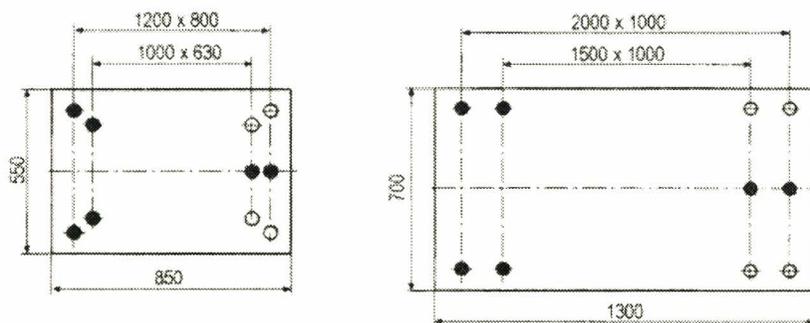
Tipos de apoyos isostáticos para mesas de planitud.
